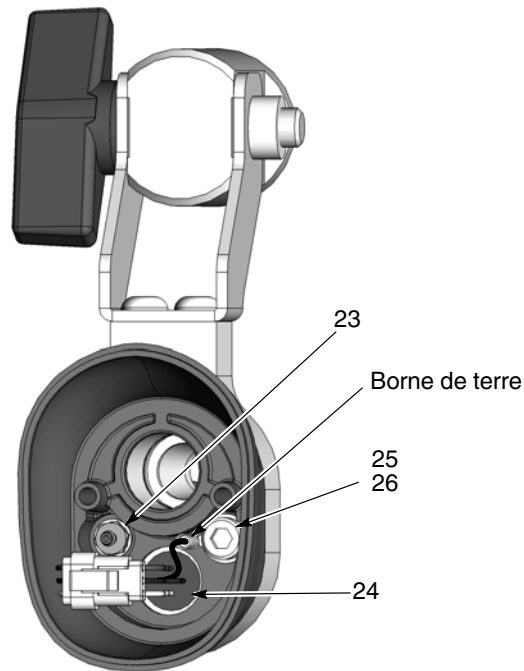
Démontage du pistolet - Remplacement de la prise du câble et du raccord cannelé
